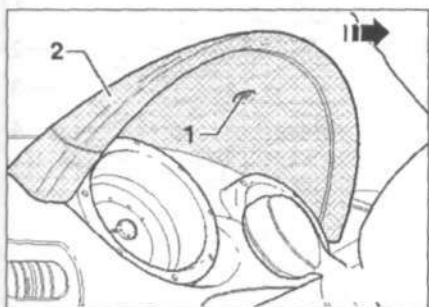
Выкрутите винт 1 и снимите верхнюю часть козырька 2 щитка приборов в направлении стрелки.
